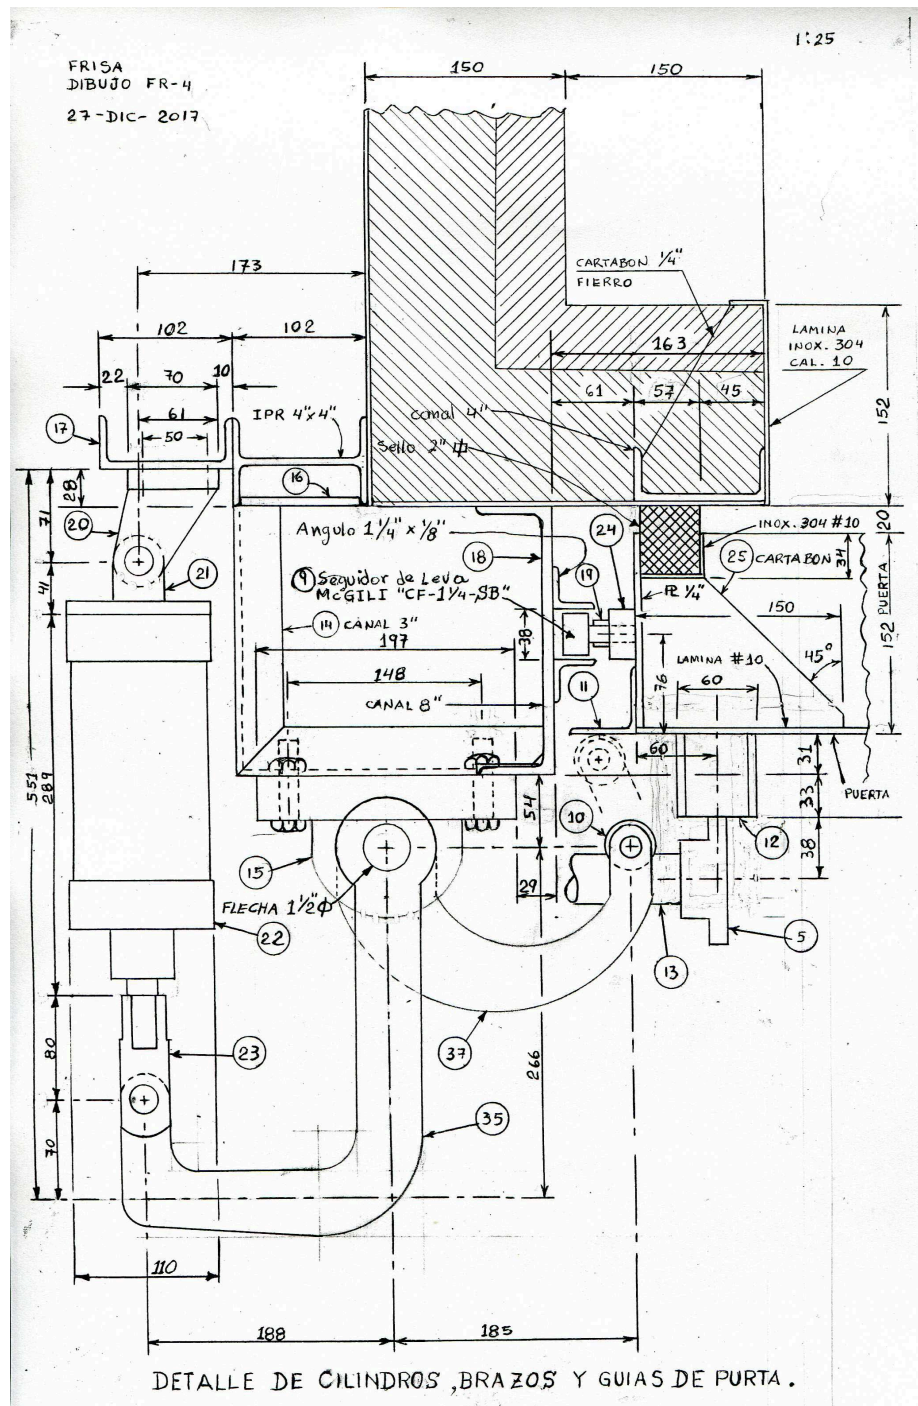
Elaboración de planos a mano alzada. Mecanismo neumático de puerta. Detalle
